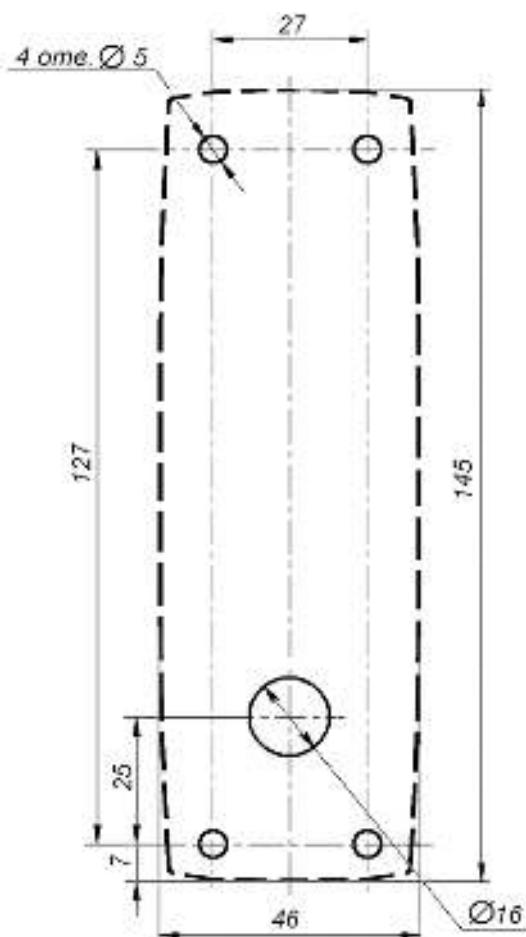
Разметка отверстий для установки считывателя (пунктиром показаны габариты корпуса считывателя)
